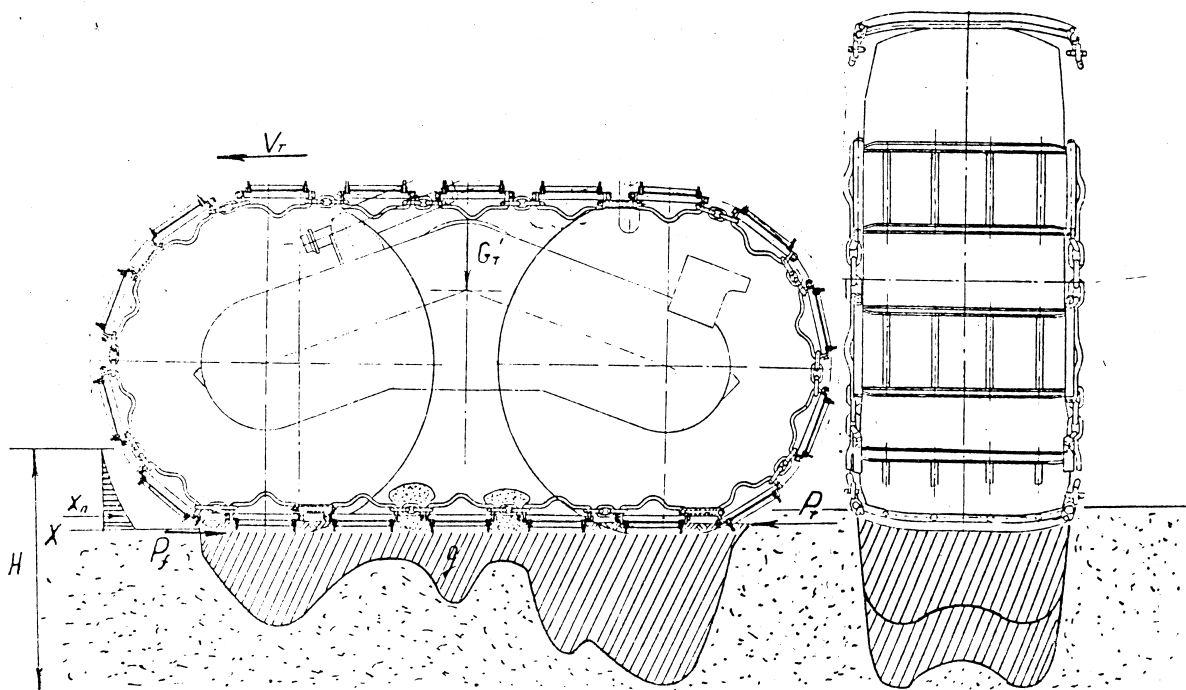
Эпюра давлений колесно-гусеничного движителя трактора ЛТ-70 на снежной целине
